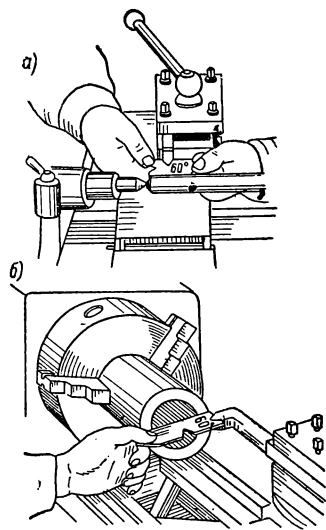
Установка резьбового резца по шаблону: а — для нарезания наружной резьбы; б — для нарезания внутренней резьбы.
